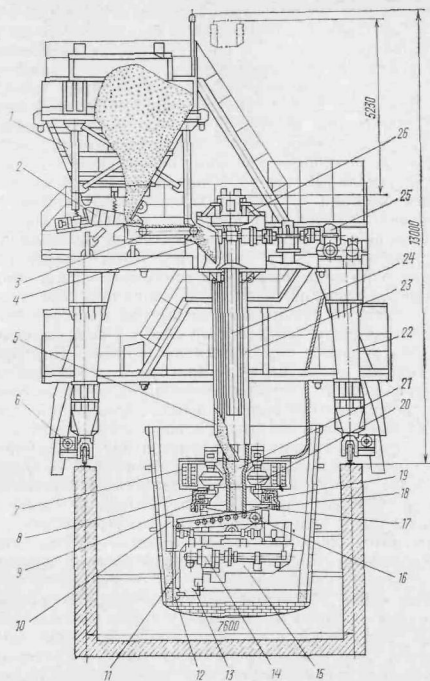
Передвижная машина «Орбита-2» для набивки футеровки ковше
